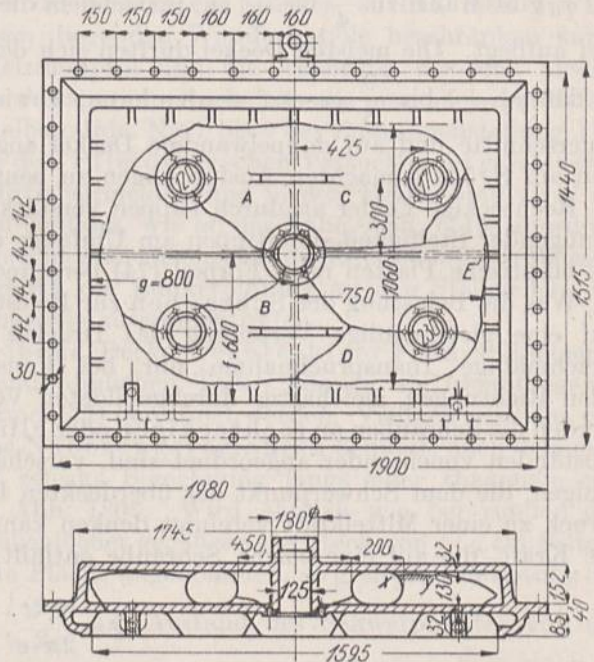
Bruch eines Schieberkastendeckels einer Walzenzugmaschine. Nach Bach. M. 1:30.
